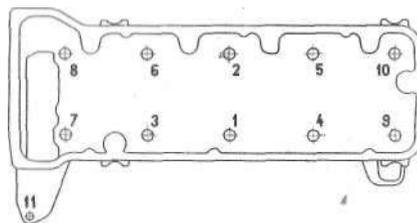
Порядок затяжки болтов крепления головки цилиндров
